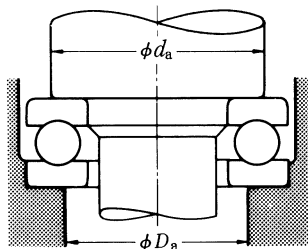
Диаметры поверхности опор для упорных шарикоподшипников
